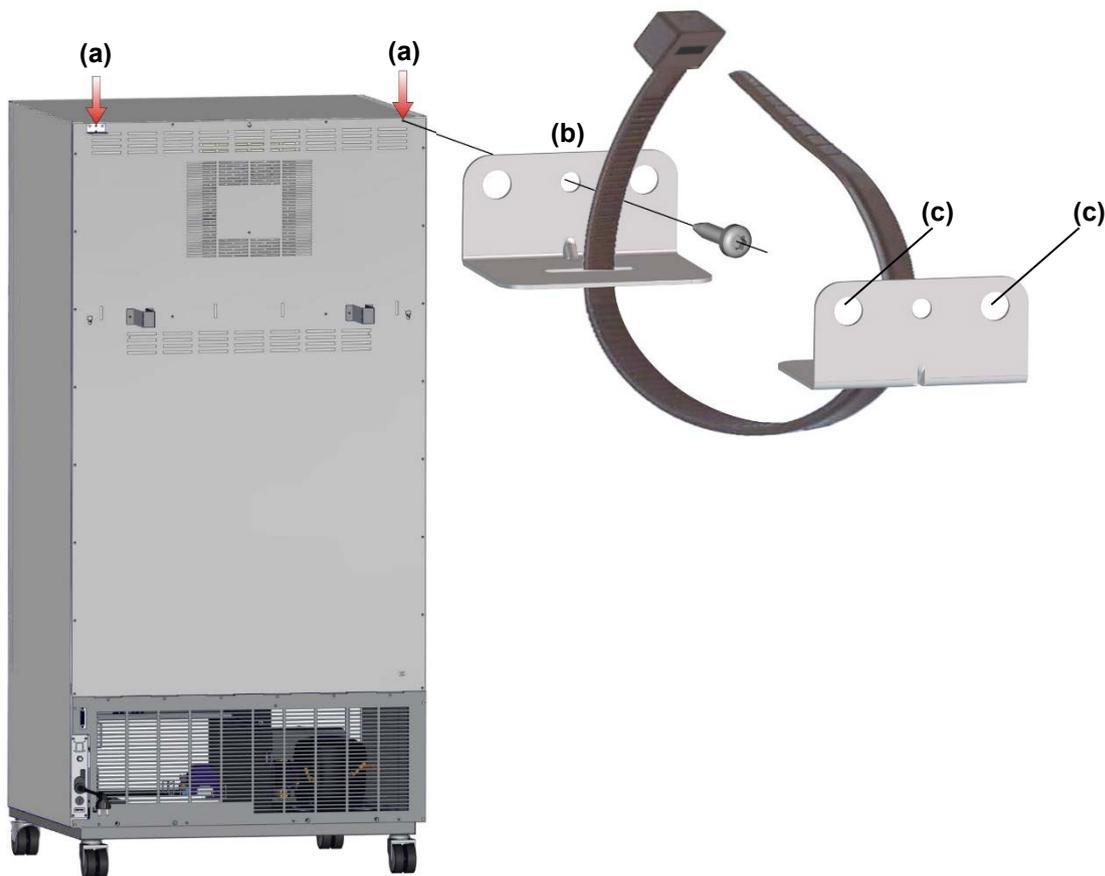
Vista posterior KBW 400 y el de la protección antivuelco flexible
